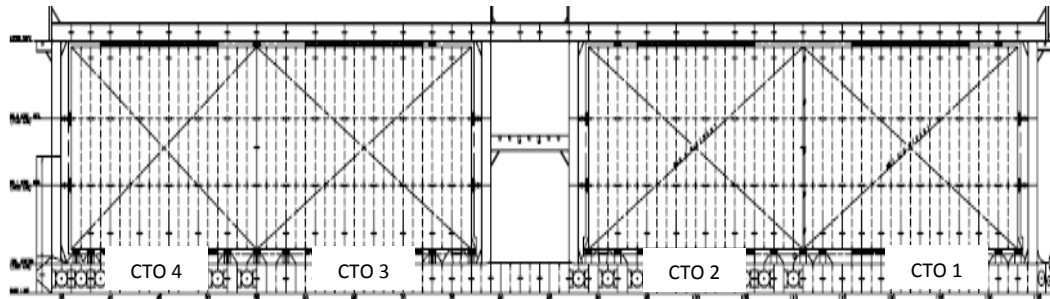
Plano diametral de tanques. Fuente: Plano de disposición de los soportes de los tanques.
